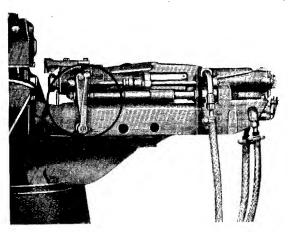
Maschine mit angebautem Lochhammer und Schalthebel für diesen
